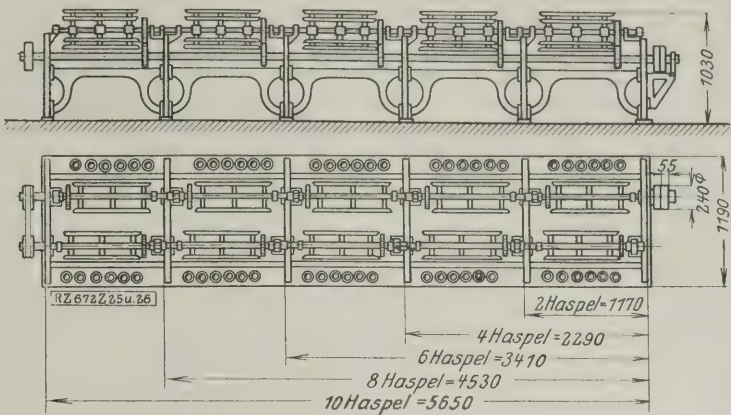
und 26. Haspelmaschine für Zentrifugen-Kunstseide.
